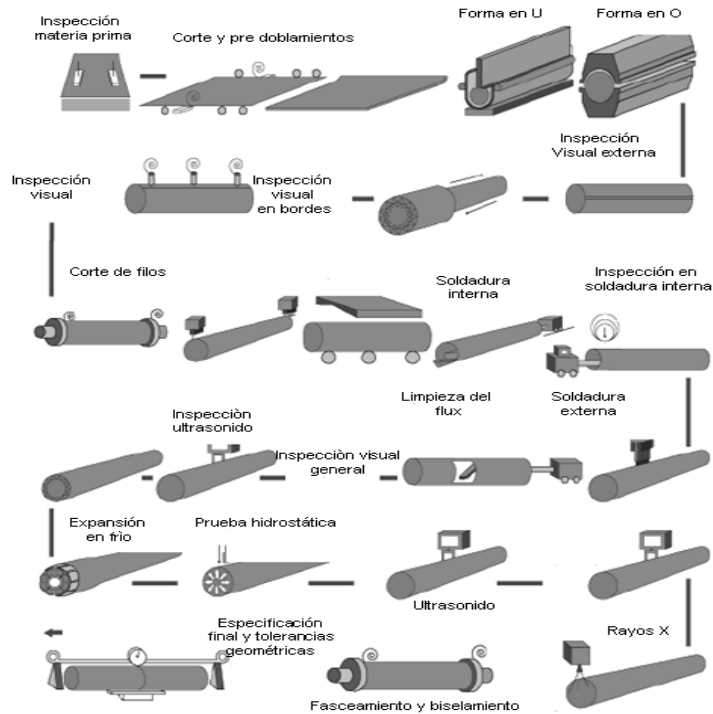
Control de calidad de fabricación de tubería para la industria petrolera por procesos de soldadura SAW y ERW [18].
